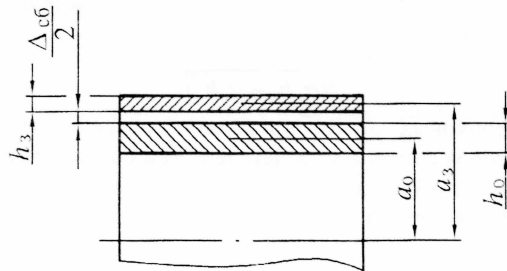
Цилиндрическая оболочковая заготовка на оправке
